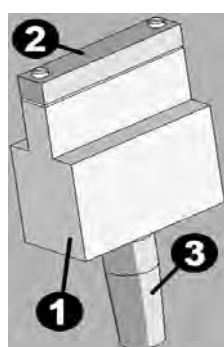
Составной электродный узел для сварки засова: 1 – бронзовая насадка; 2 – медная накладка; 3 – электрод с конической поверхностью
